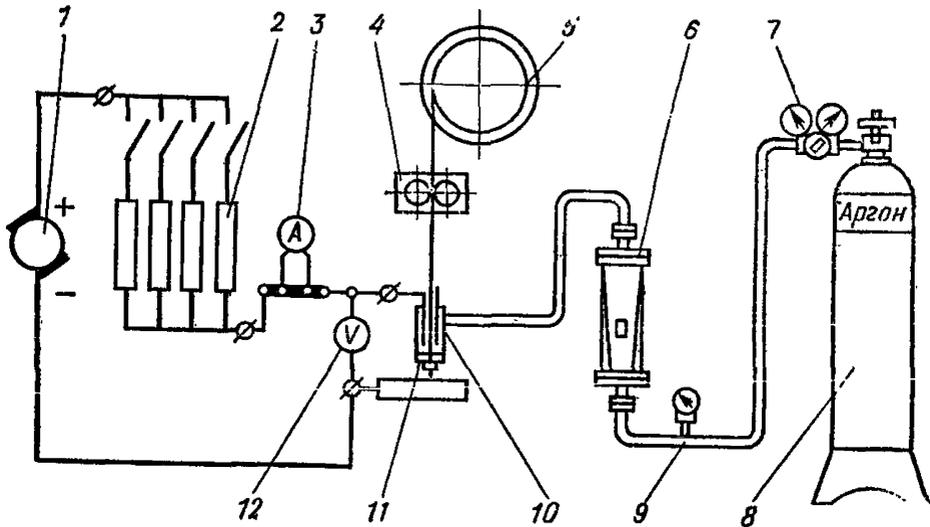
Схема поста автоматической или полуавтоматической сварки плавящимся электродом
